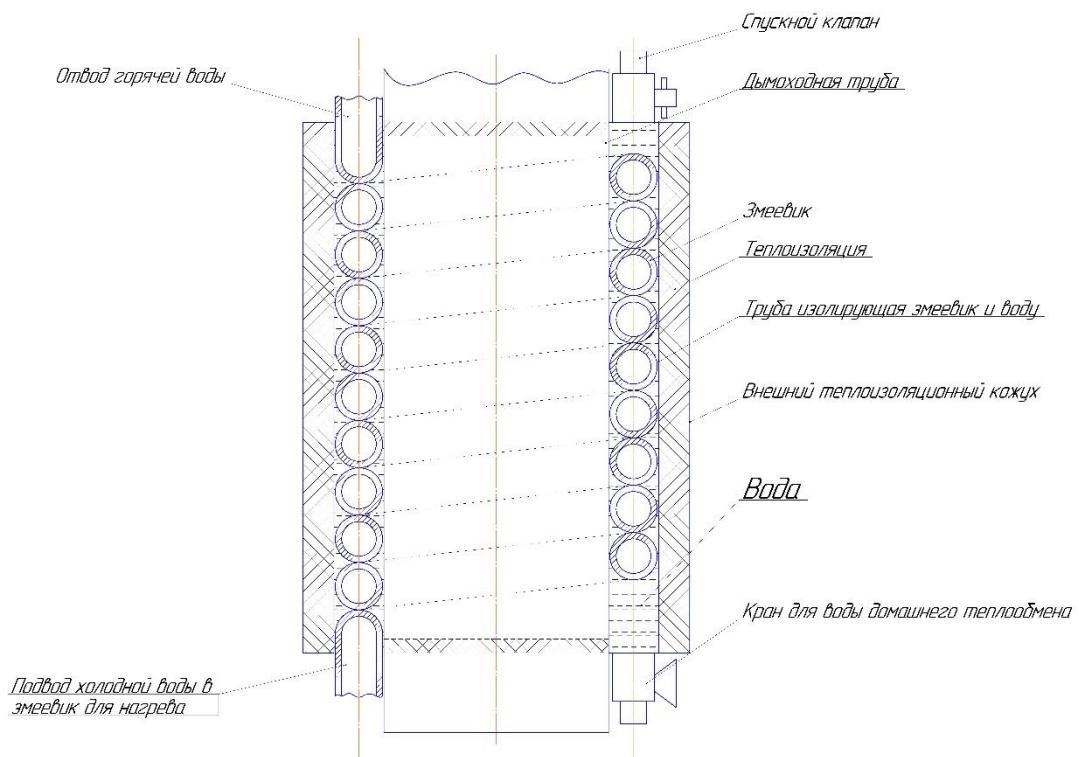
Эскиз в разрезе проточного водонагревателя на дымоходной трубе.
